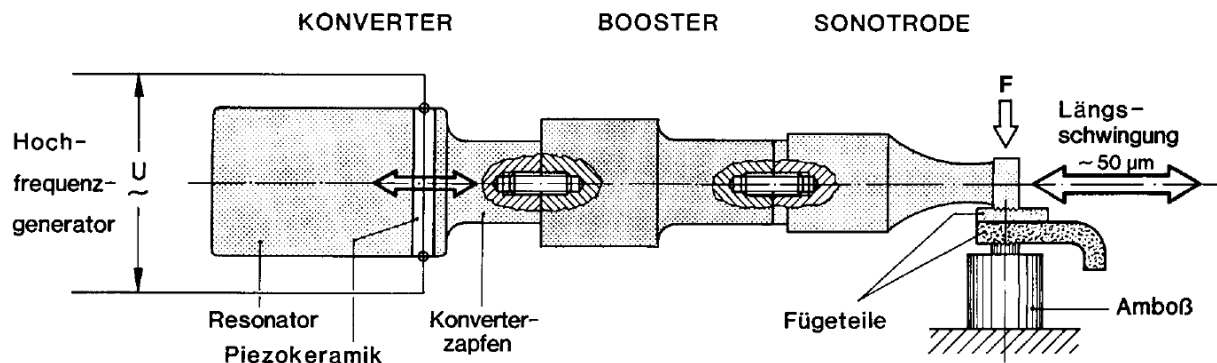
Prinzipskizze Ultraschallschweißen
